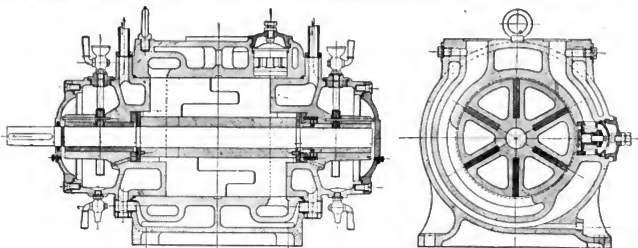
Z. A.: Die neue Rundstempelmaschine.
